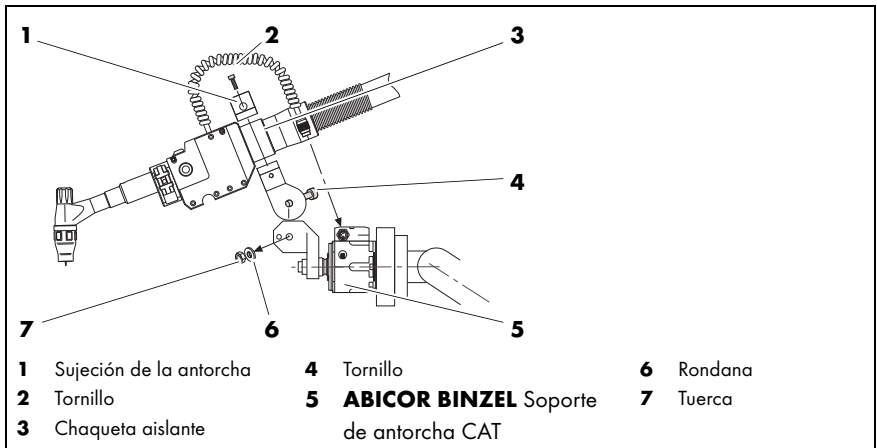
Montar la antorcha de soldadura TIG en el robot
